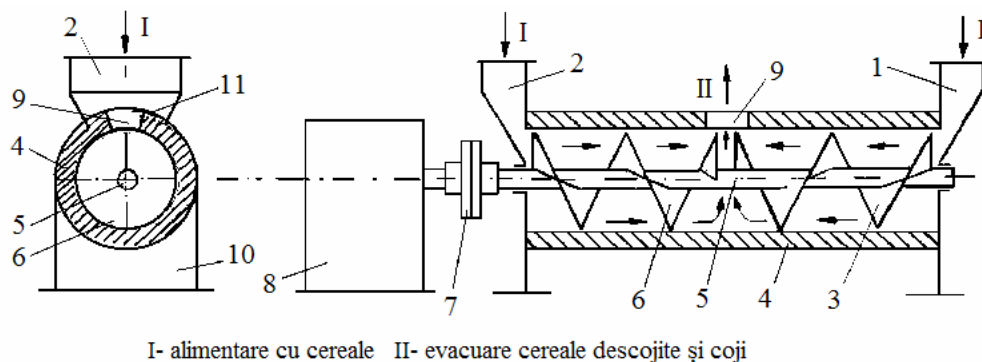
Schema descojitorului intensiv cu melci: 1,2- gură alimentare; 3- melc dreapta, 4- carcasă cilindrică abrazivă; 5- ax antrenare; 6- melc stînga; 7- cuplaj elastic; 8- motoreductor; 9- fereastră evacuare; 10- suport sprijin; 11- clapete reglaj
